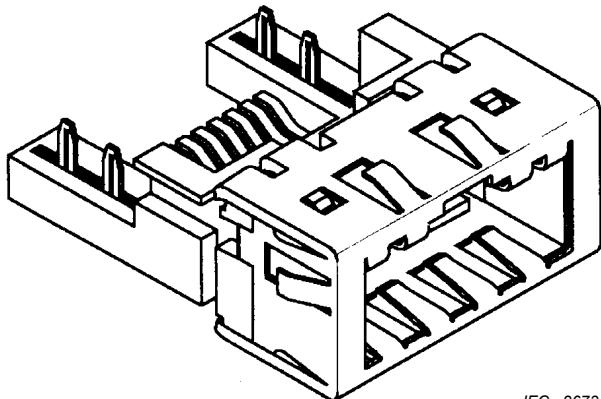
Vue de face de l'embase (XB), montage à cheval sur carte (version 1) (TA)
